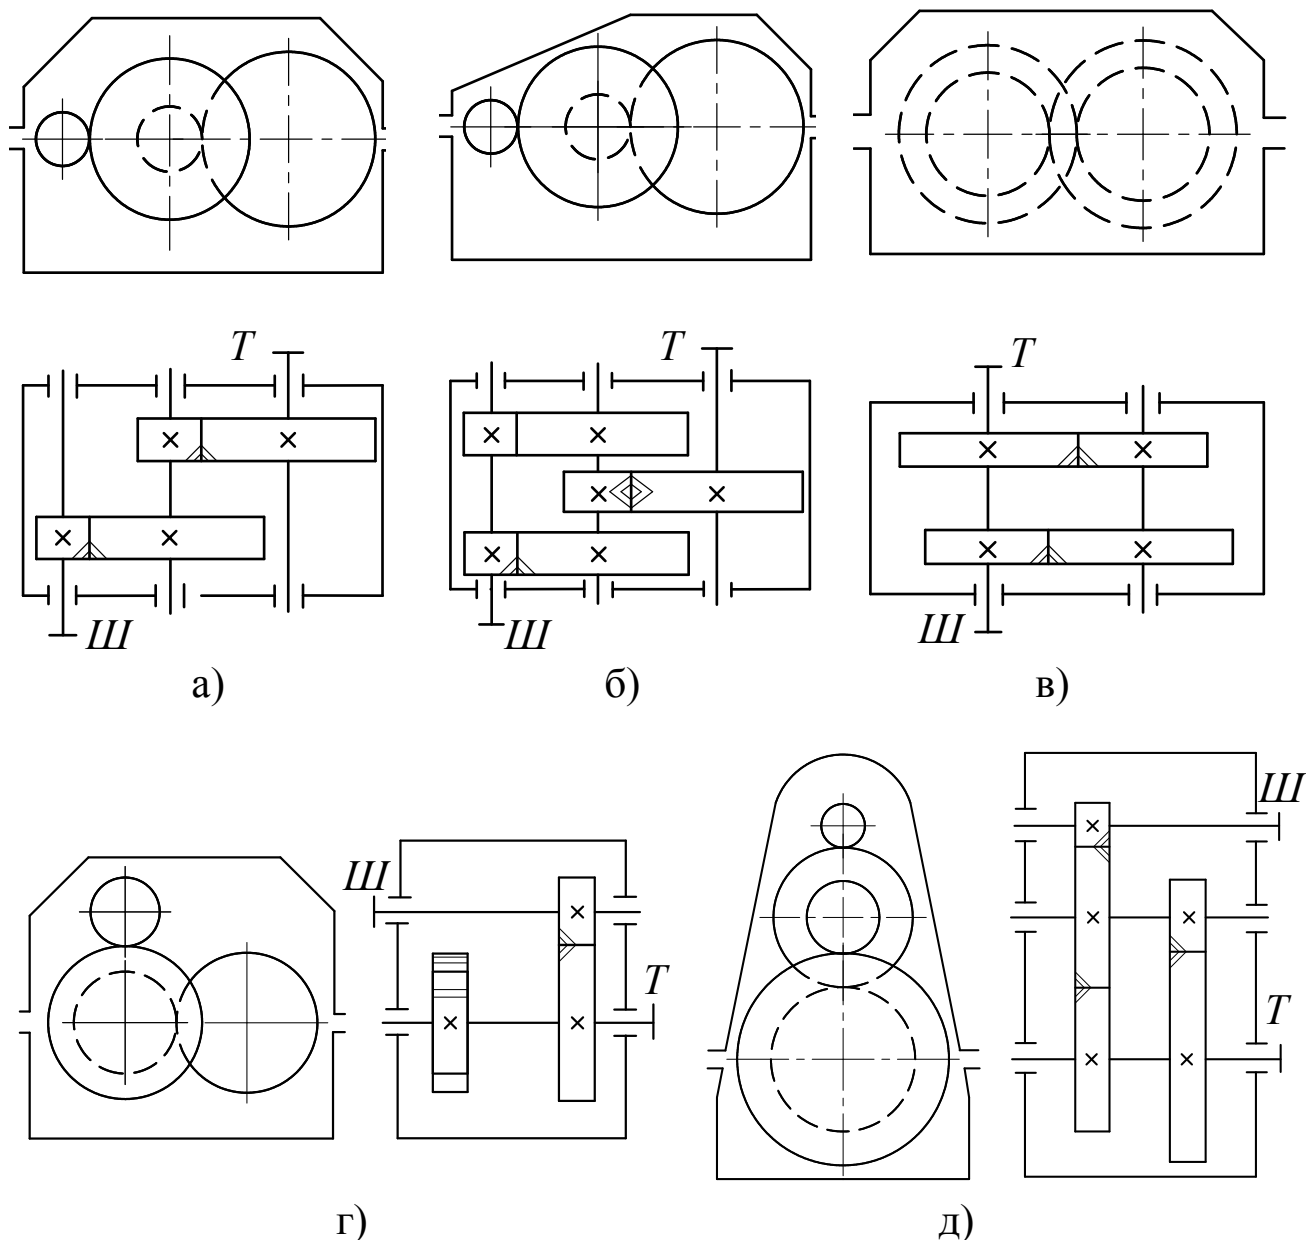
Кинематические схемы двухступенчатых цилиндрических редукторов: а) развернутая схема; б) развернутая схема с раздвоенной первой ступенью; в) соосный редуктор; г) вертикально-горизонтальный редуктор; д) вертикальный редуктор, (*Ш* – быстроходный вал, *T* – тихоходный вал)
